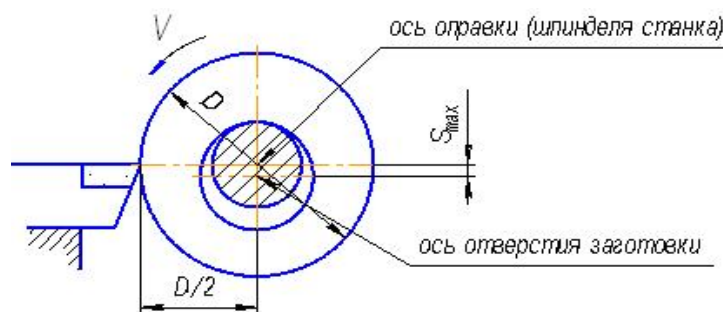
Схема формирования параметров детали при ее обточке с установкой на оправке с гарантированным зазором
